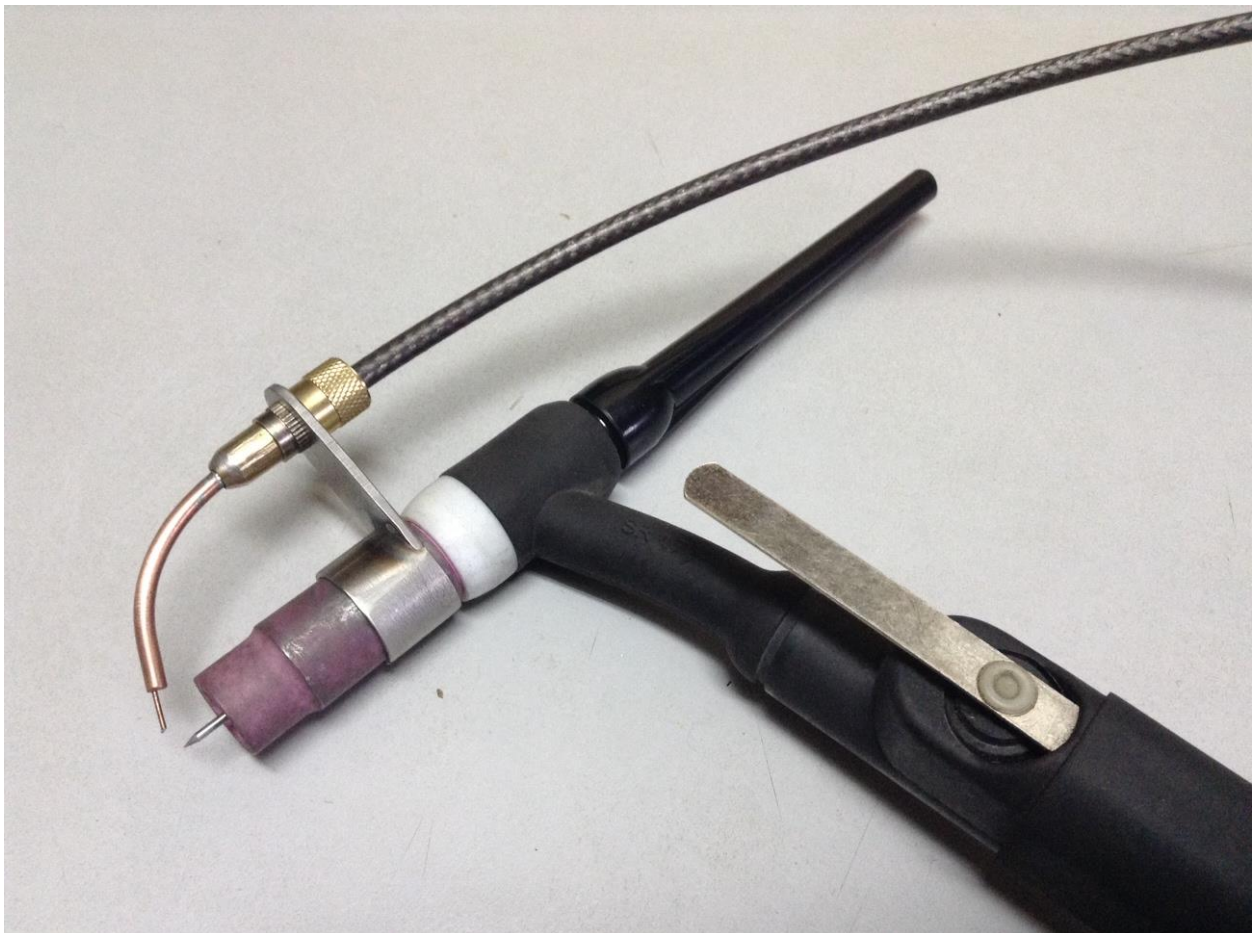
Горелка для TIG сварки при механизированной подаче проволоки
